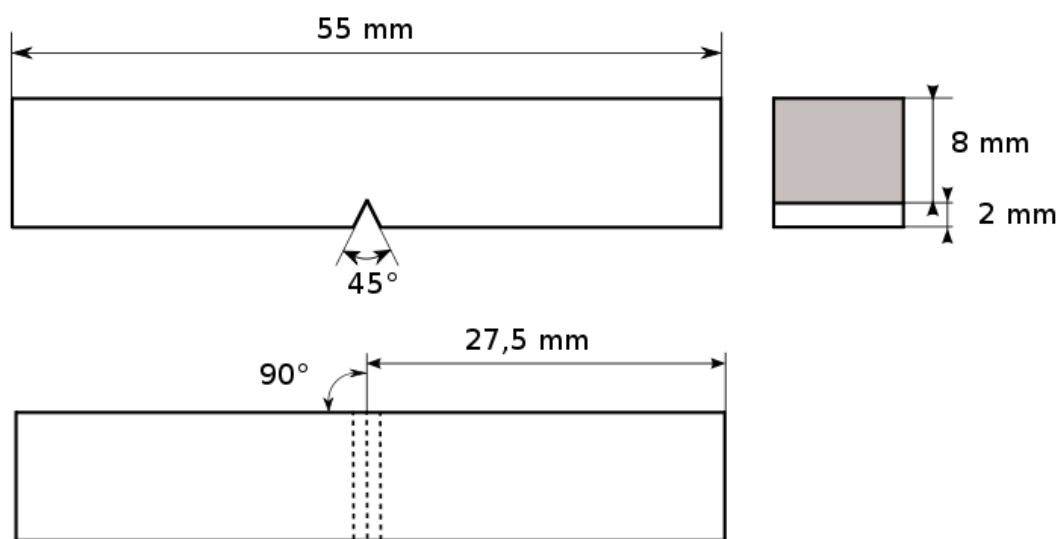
Dimension et forme de l'éprouvette Charpy.
